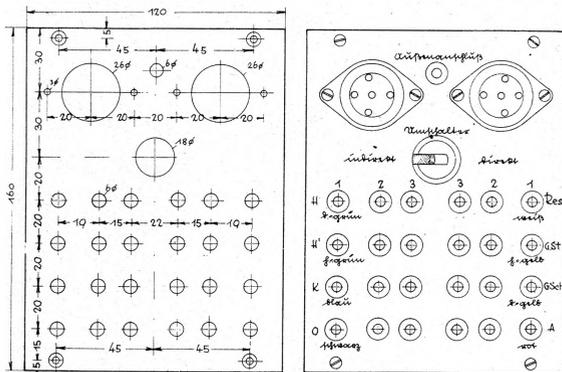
Bohr- und Montageplan für die Deckplatte.
